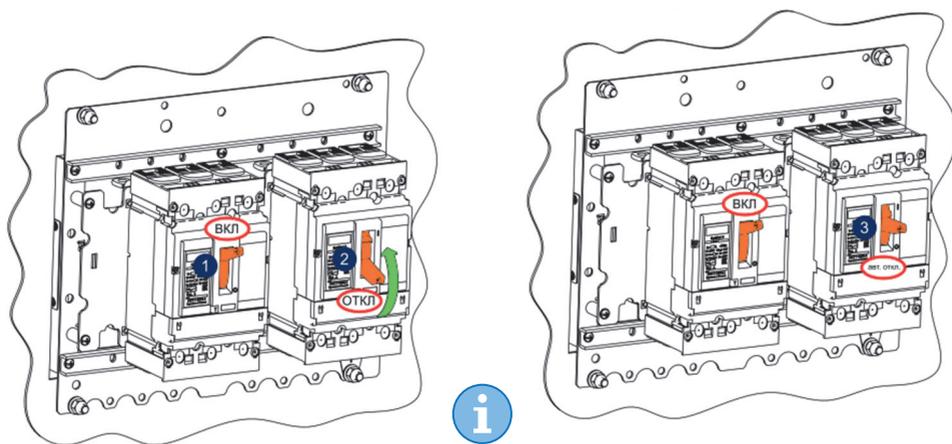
Установка подготовленного стационарного выключателя на раму механической блокировки
